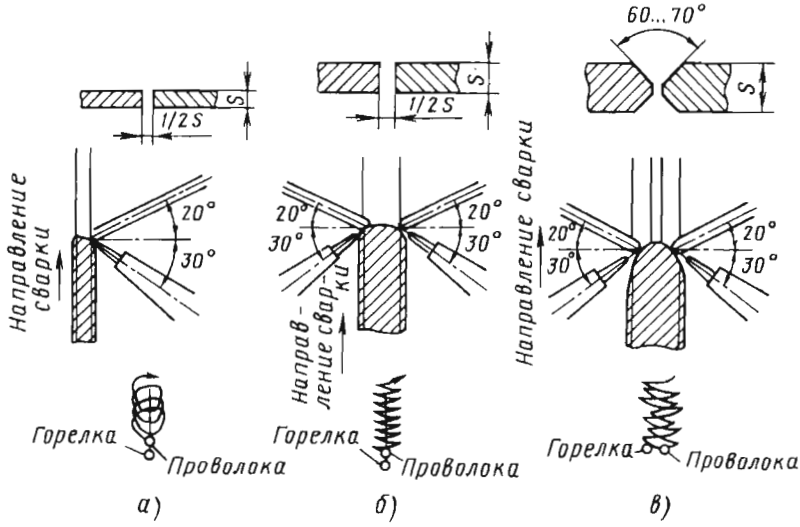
Схемы сварки сквозным валиком при толщине металла, мм:
